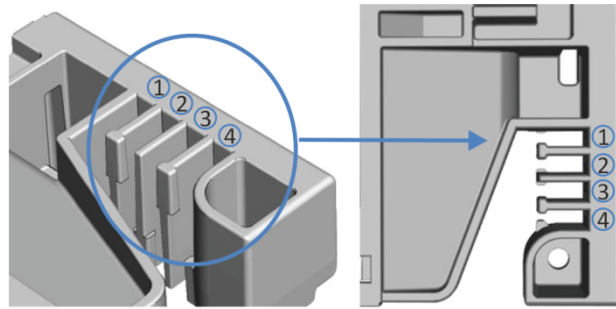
Schlauchkanal mit Schlauchführungen (links: Ansicht von innen, rechts: von oben)
